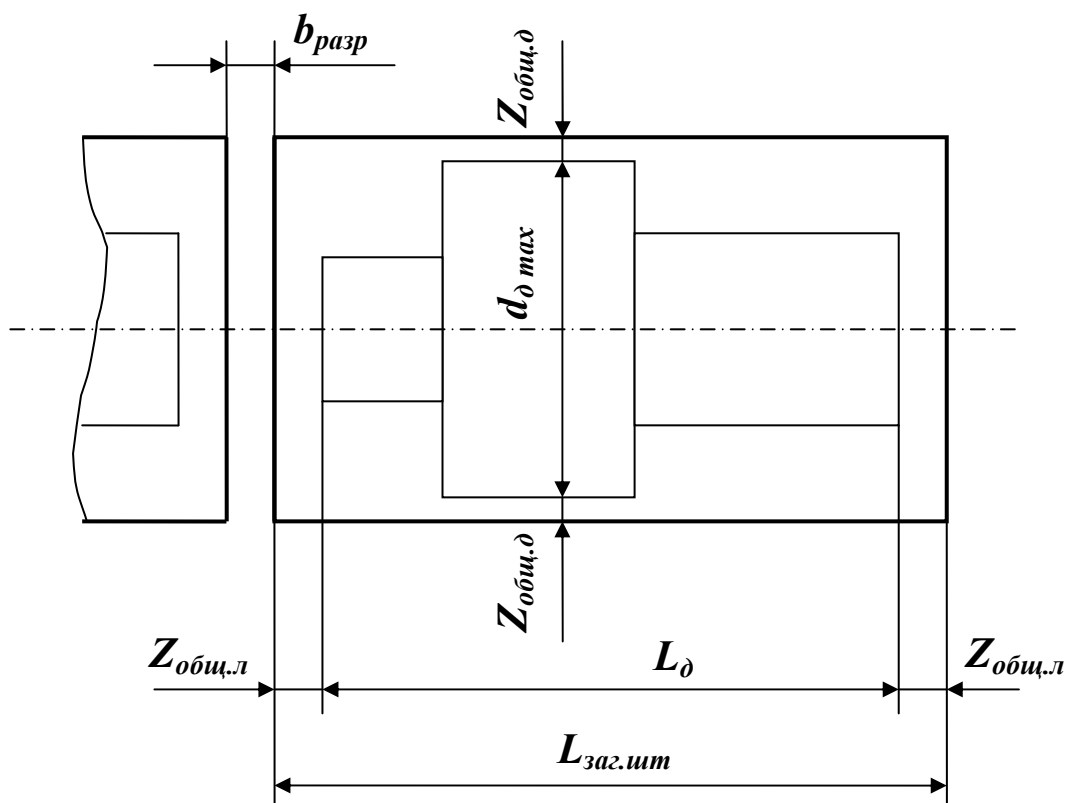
Эскиз заготовки из круглого проката для детали типа „вал ступенчатый”.
